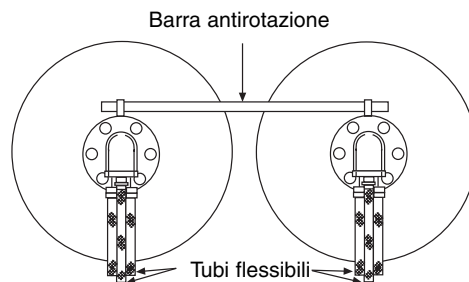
Installazione della barra antirotazione nell'aletta sul corpo.
